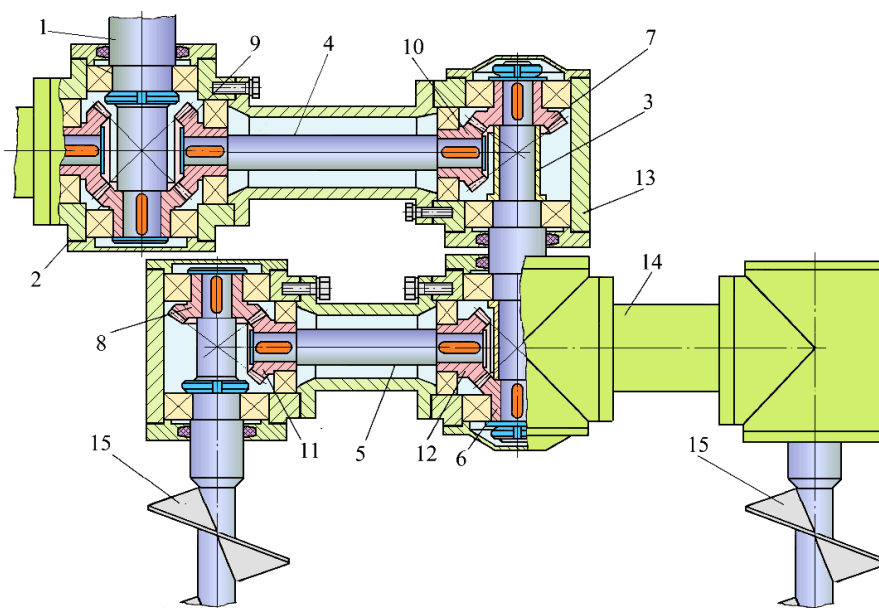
Элементы конструкции привода цилиндрического бипланетарного смесителя:
